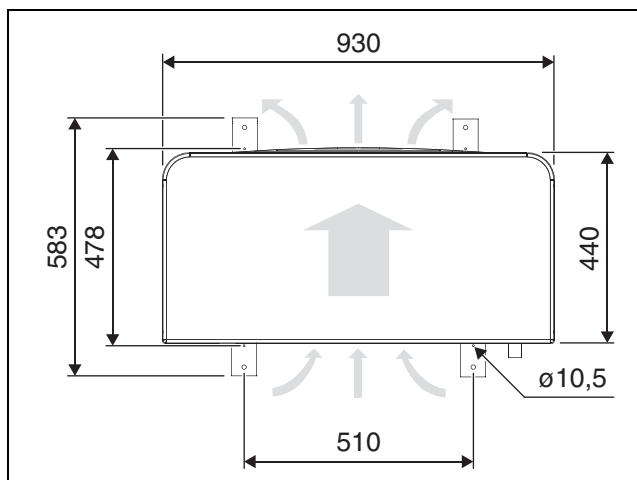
Dimensions des modèles de pompe à chaleur 5-9, vue du dessus
